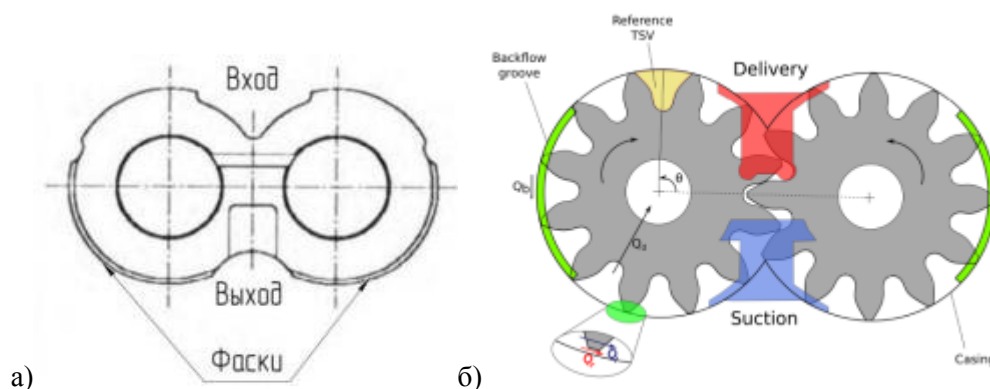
Схемы разгрузочных устройств: а) опорный блок (внутренняя часть) [4], б) вид блока шестерней с разгрузочно-распределительными устройствами [5]
